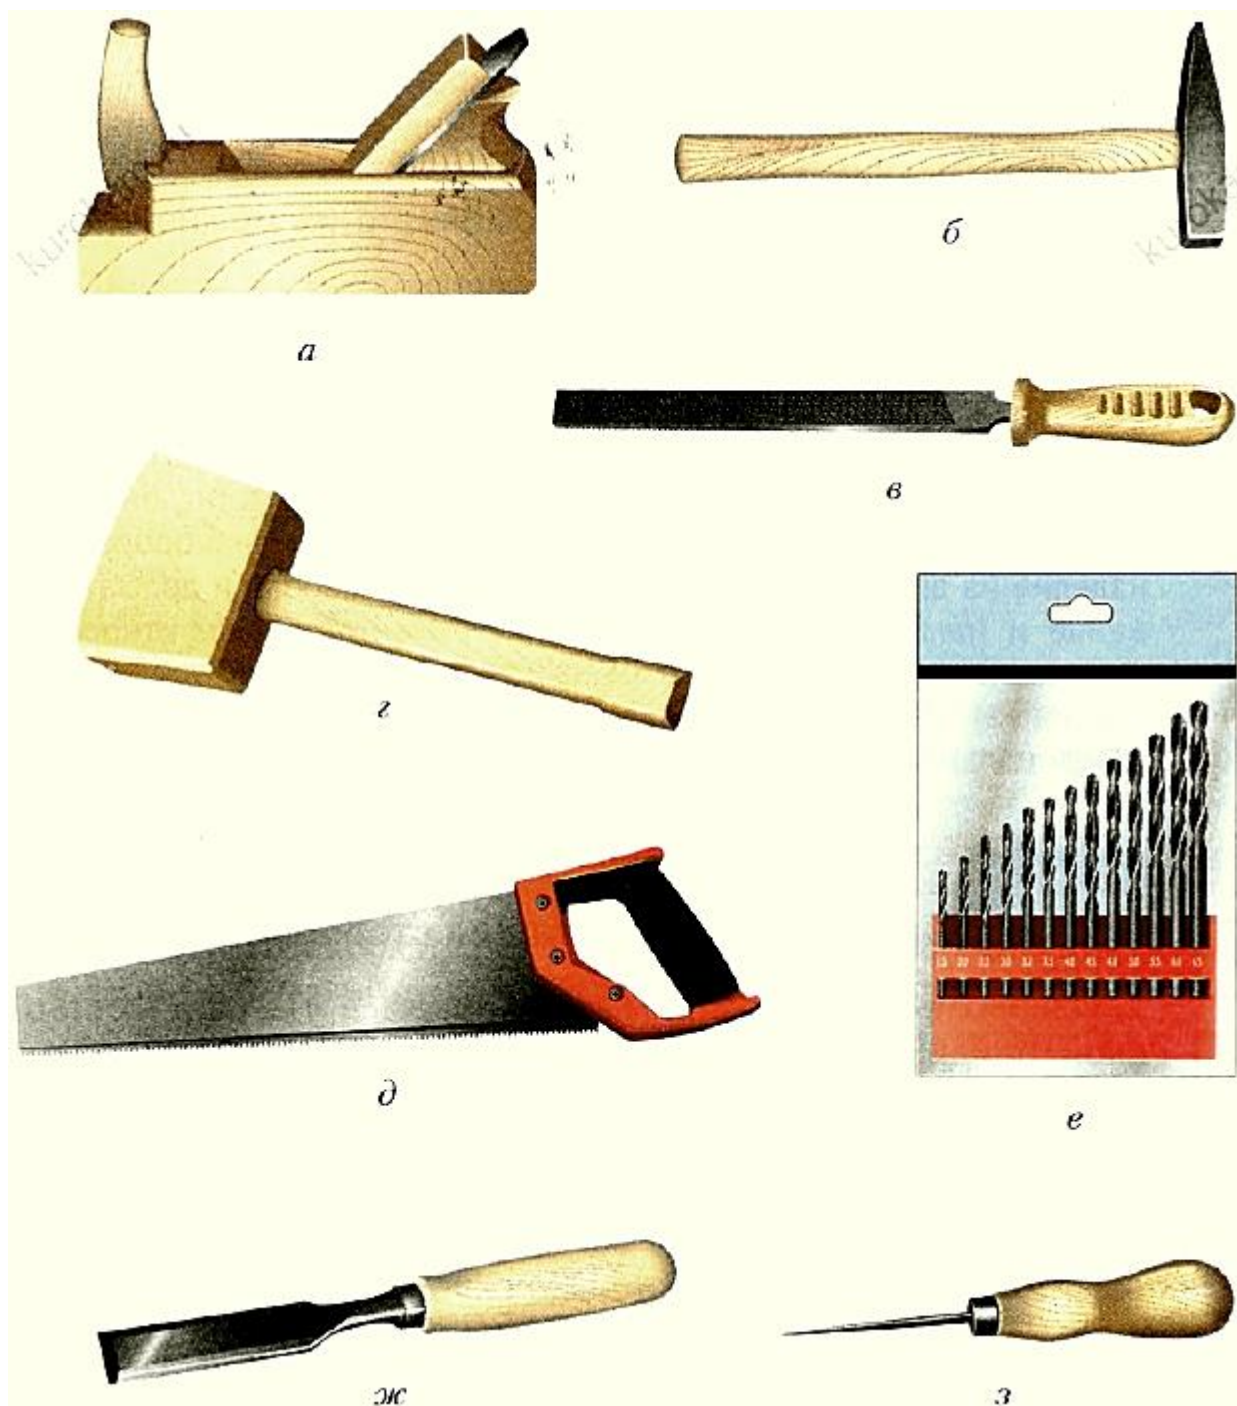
Основные инструменты для обработки древесины: а — рубанок; б — молоток; в — напильник; г — киянка; д — ножовка; е — свёрла; ж — стамеска; з — шило
